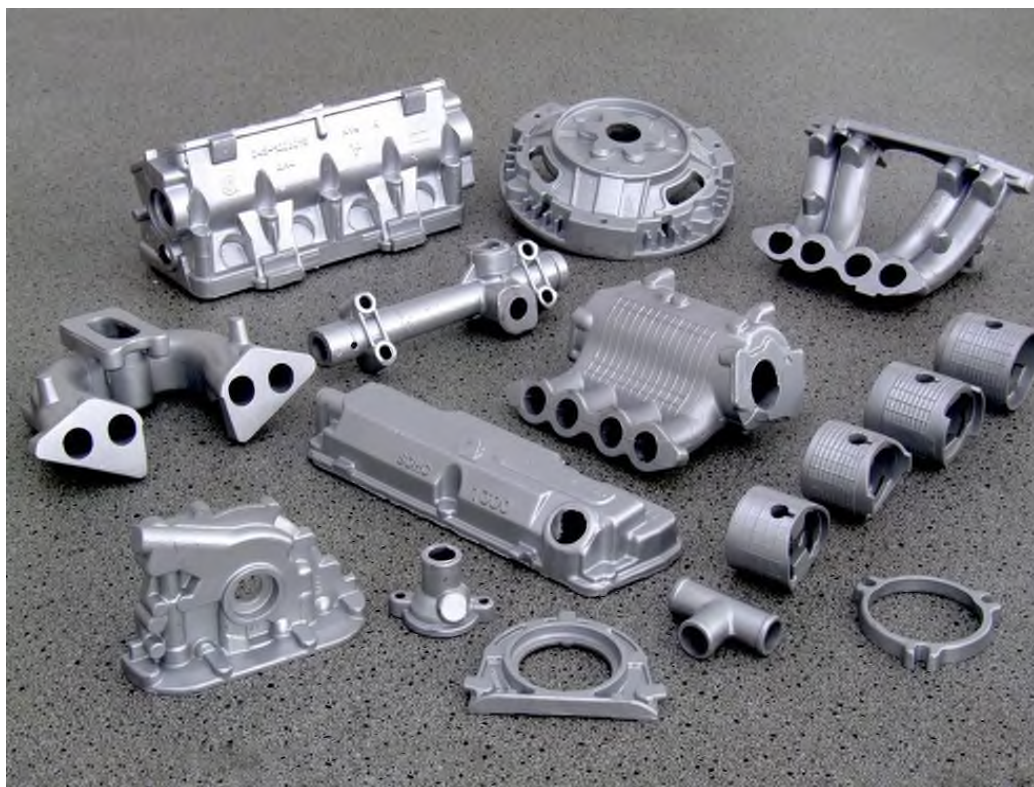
Литые заготовки для двигателей внутреннего сгорания из алюминиевых сплавов
